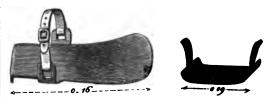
Semelle en fer (à gauche) et demi-semelle.
